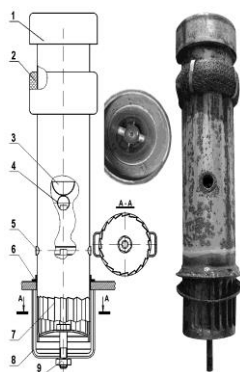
Центробежный массообменный элемент, типа (1 – каплесьемник; 2 – сетчатая насадка; 3 – вытеснитель; 4 – трубка рециркуляции газа; 5 – трубка рециркуляции жидкости; 6 – корпус элемента с фланцем; 7 – тангенциальный завихритель; 8 – скоба; 9 – шпилька).
